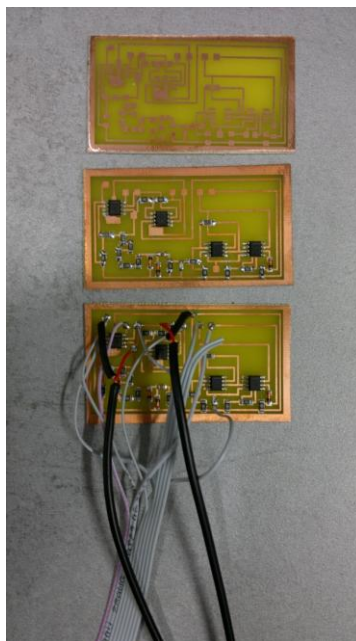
Univerzální plošný spoj použitý pro testy
